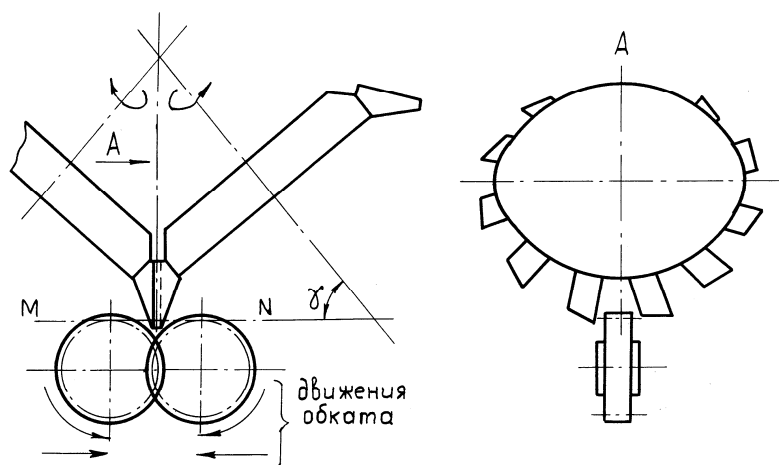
Схема процесса зубонарезания цилиндрических колес дельтовидными резцовыми головками.
